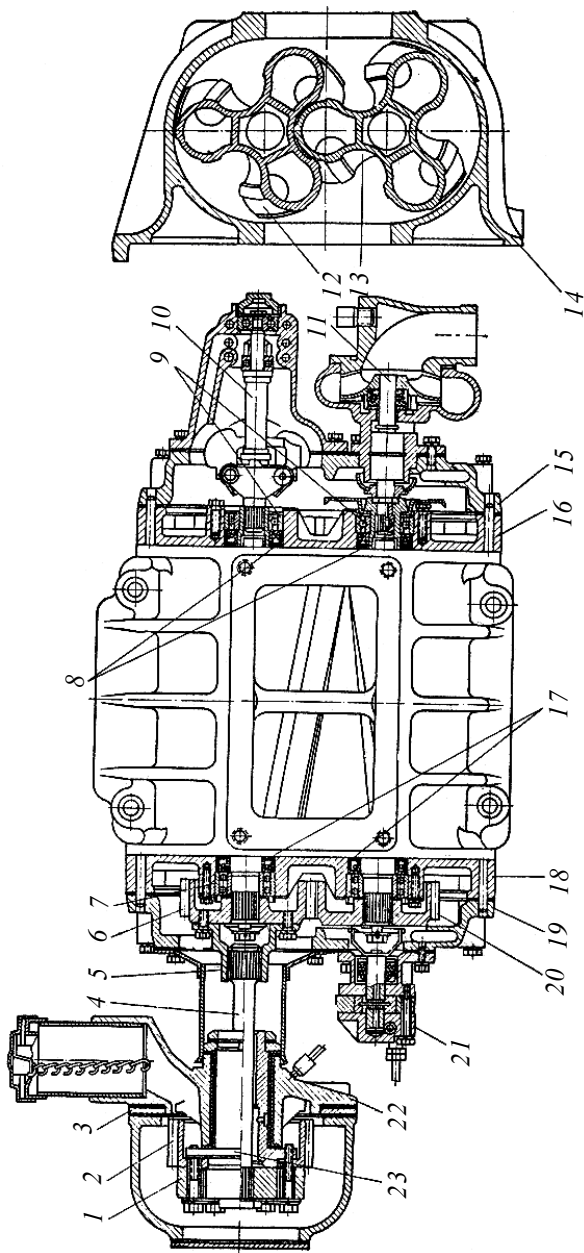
Подовжній і поперечний розрізи роторно-лопатєвого компресора двигуна ЯАЗ-204:
